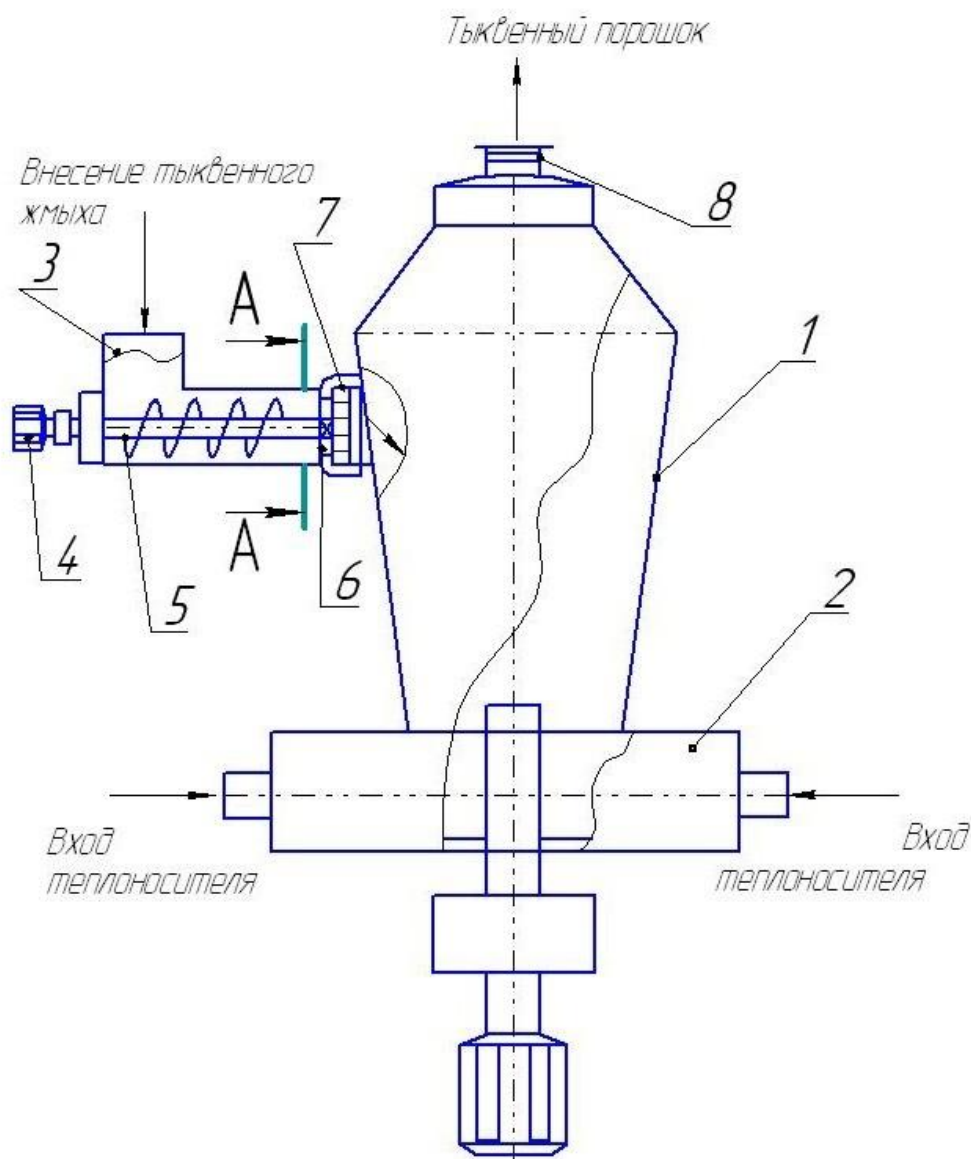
Внешний вид установки для сушки и измельчения тыквенного жмыха
